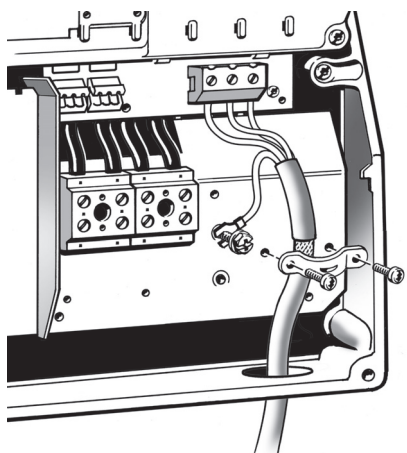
Motoranschluss, Gehäuse B1 und B2
